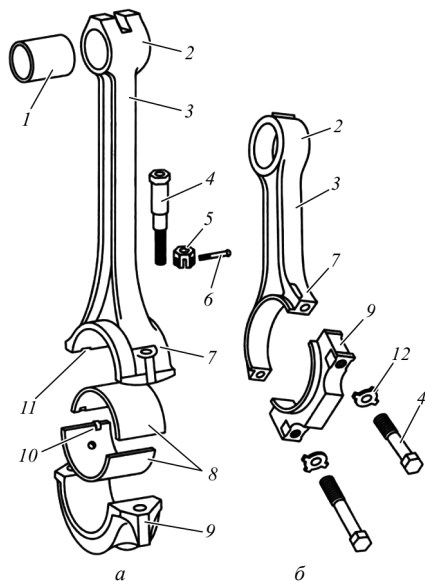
Конструкция шатунов: *а* – шатун с прямым разъемом; *б* – шатун с косым разъемом; 1 – втулка поршневого пальца; 2 – верхняя головка шатуна; 3 – стержень; 4 – шатунный болт; 5 – гайка; 6 – шплинт; 7 – нижняя головка шатуна; 8 – вкладыши шатунного подшипника; 9 – крышка; 10 – усик вкладыша; 11 – паз нижней головки шатуна; 12 – замковая шайба
